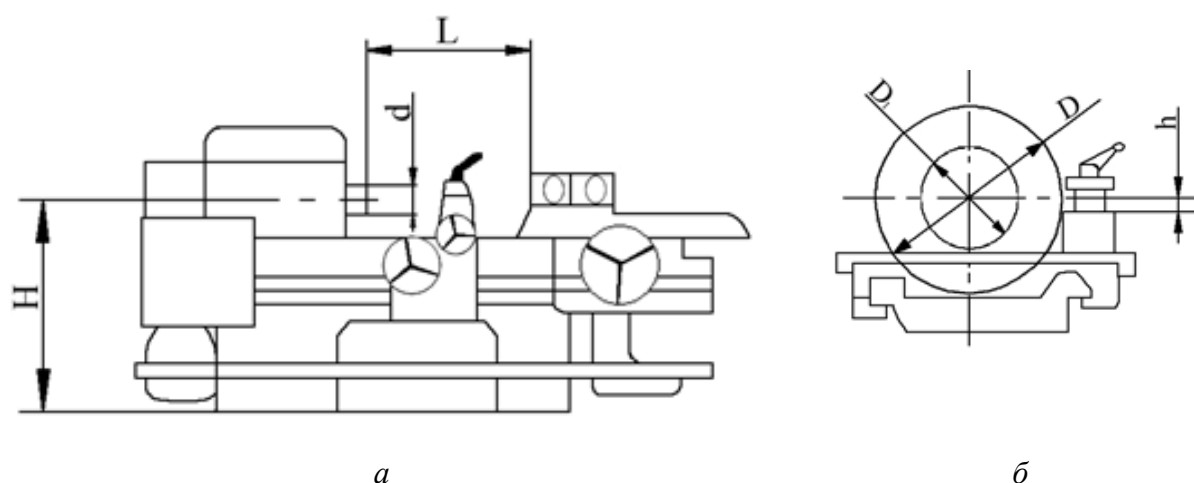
Общий вид токарно-револьверного станка (а) и вид сбоку на его рабочую зону (б)
